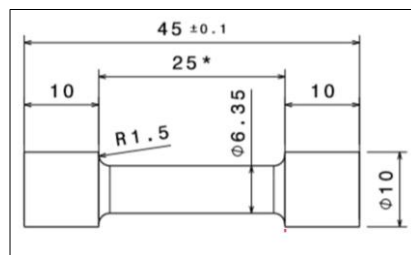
Detalle de las dimensiones de una muestra a extraer
